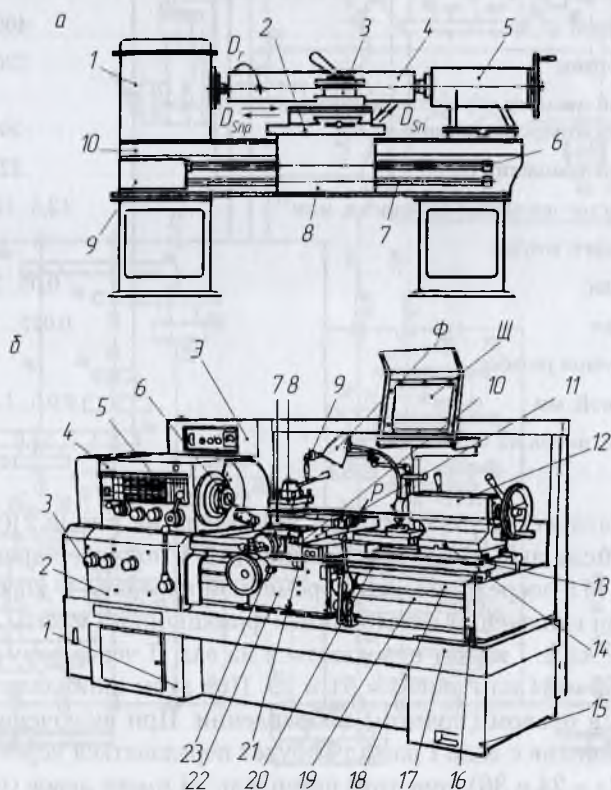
Схема токарно-винторезного станка (а) и общий вид станка мод. 16К20 (б)
